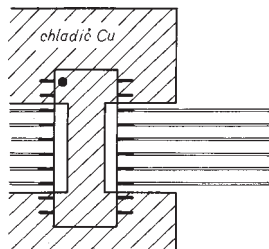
, b, c. Mechanické provedení pouzdra PWP
